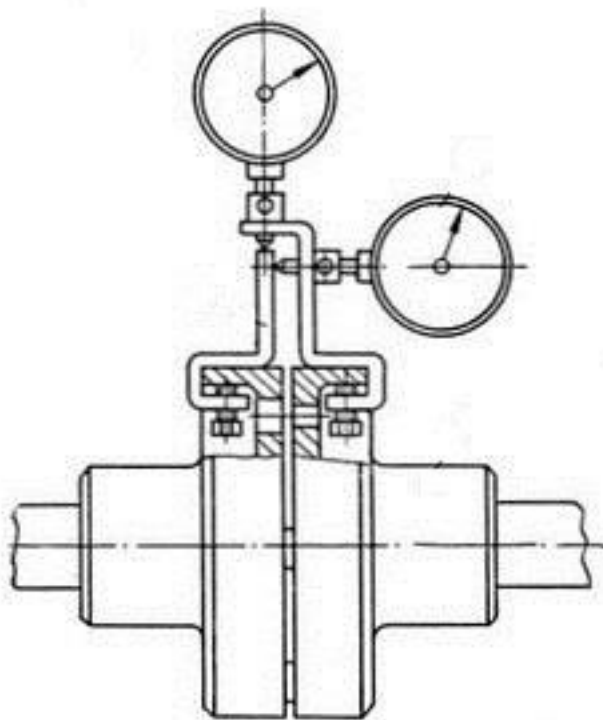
Приспособление для центровки упругих втулочно-пальцевых муфт
